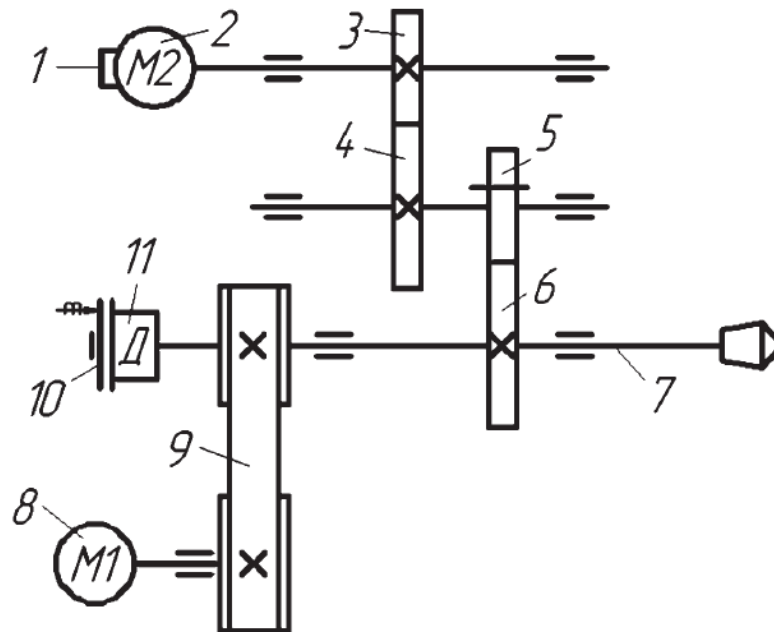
Кінематична схема приводу позиціонування шпинделя від серводвигуна через ковзну шестерню
